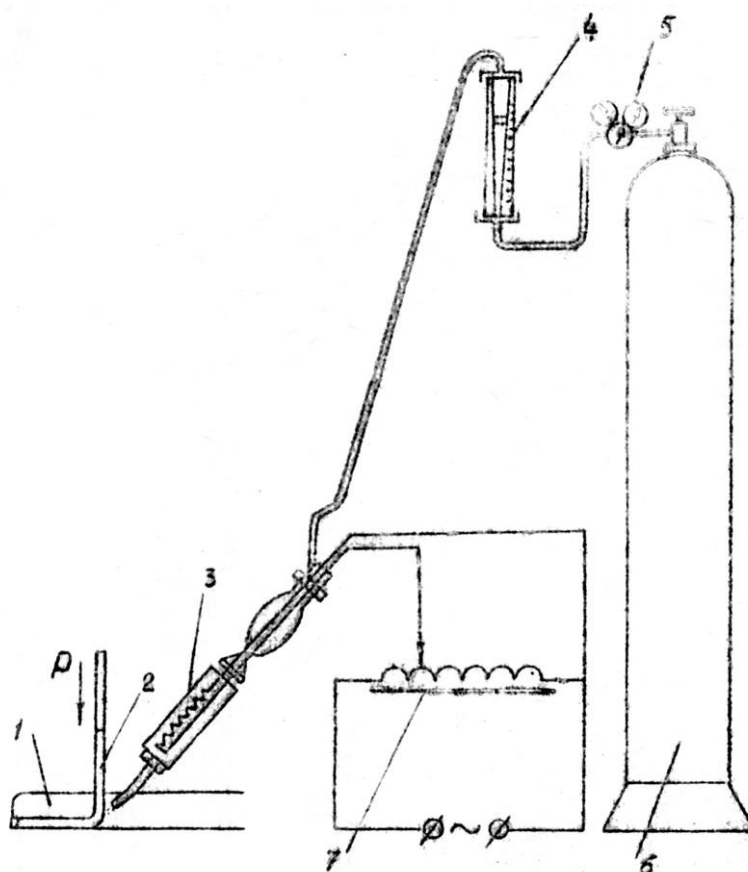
Схема поста для сварки пластмасс горячими газами:
